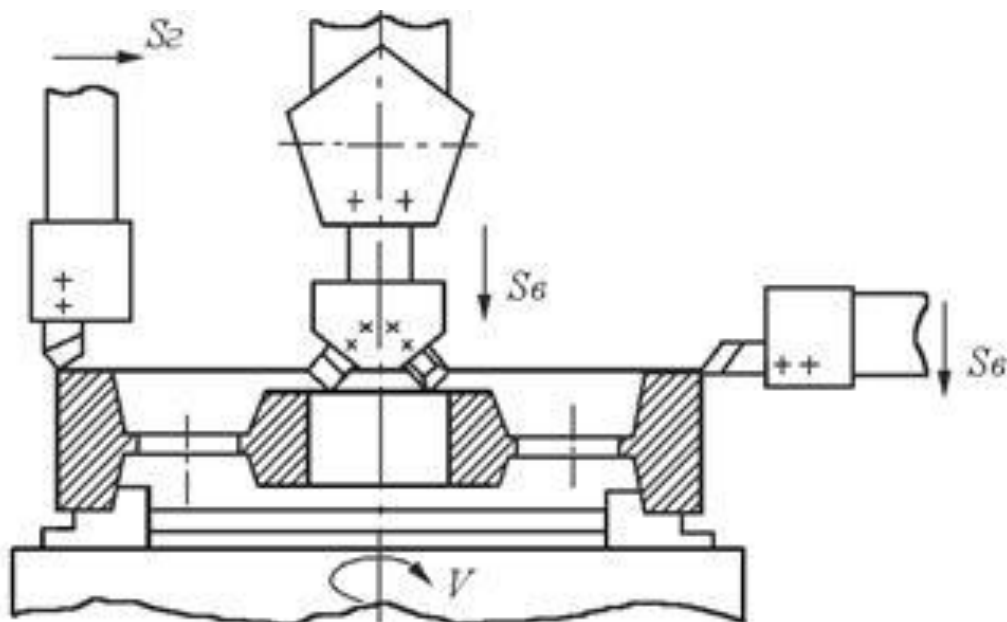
Схема обработки заготовки на токарно-карусельном станке
